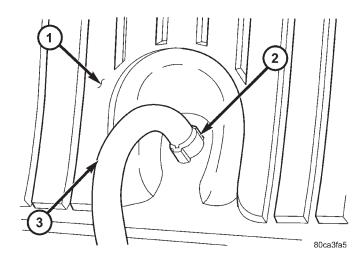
Desmontaje e instalación de boquilla de lavador delantero
